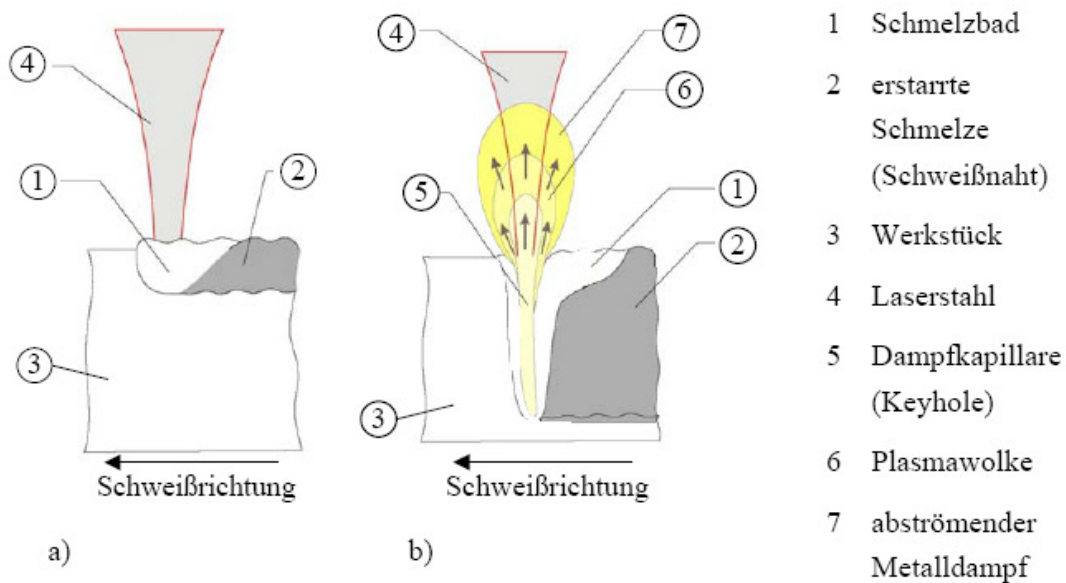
Prinzip des Wärmeleitungsschweißens a) und des Tiefschweißens b) [6]
